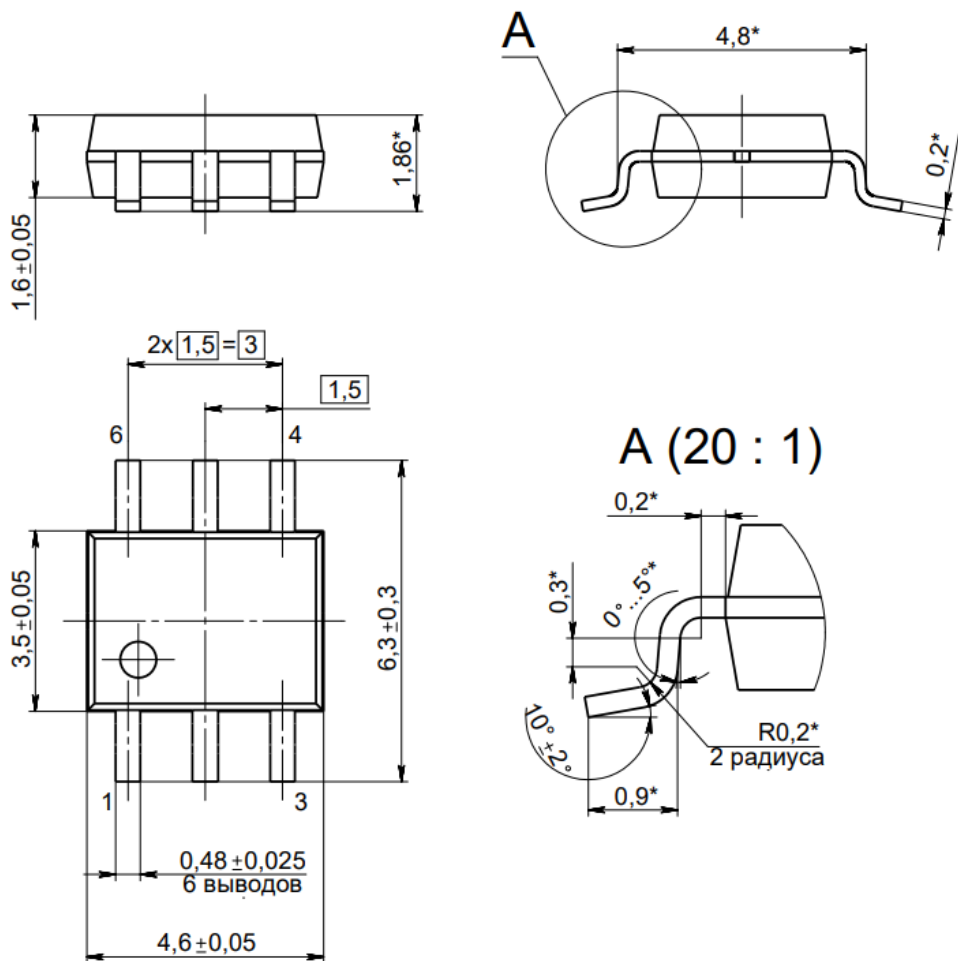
Габаритный чертеж корпуса 4341.6-1 К (размеры в мм)
